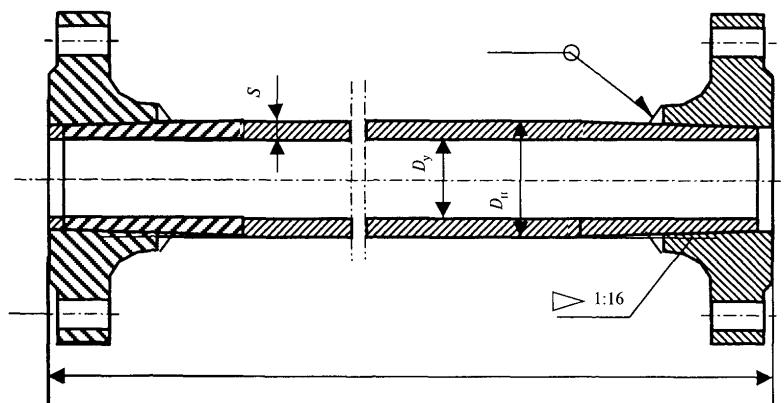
Схема трубы с приваренными фланцами (тип Б)
